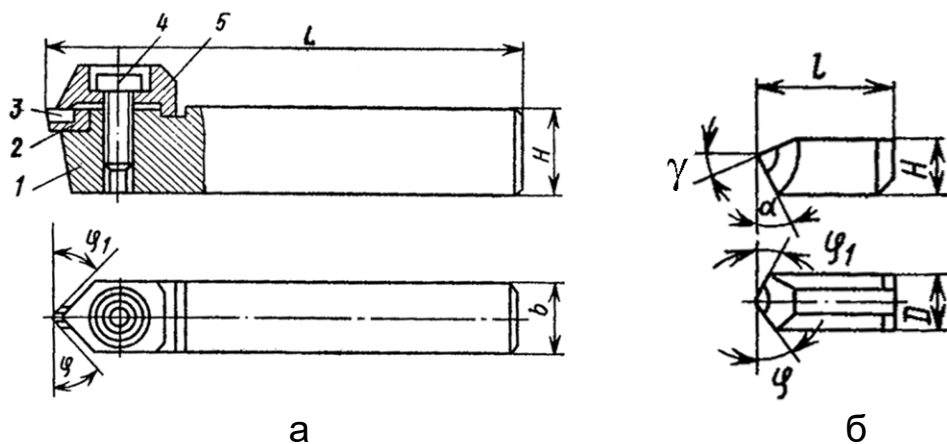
Сборный резец, оснащенный вставкой из СТМ:
